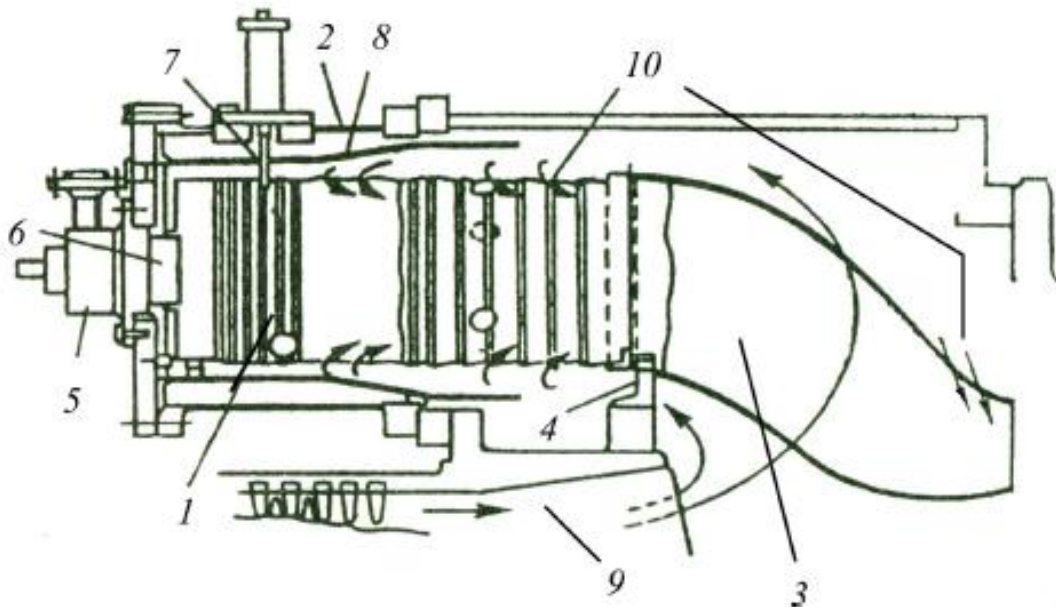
Виносна камера згоряння фірми General Electric: 1 – жарова труба; 2 – зовнішній корпус (окремий для кожної жарової труби); 3 – газозбірник; 4 – опора; 5 – фронтний пристрій; 6 – форсунка; 7 – свічка запалення; 8 – дефлектор; 9 – повітря із-за компресору; 10 – охолоджуюче повітря.
